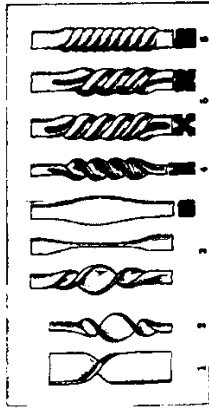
Типы скруток из: 1 — плоской заготовки; 2 — раскованной круглой заготовки; 3 — раскованной квадратной заготовки; 4 — плоской заготовки с «аборничкой»; 5 — квадратной заготовки с двумя «аборничками»; 6 — квадратной заготовки
